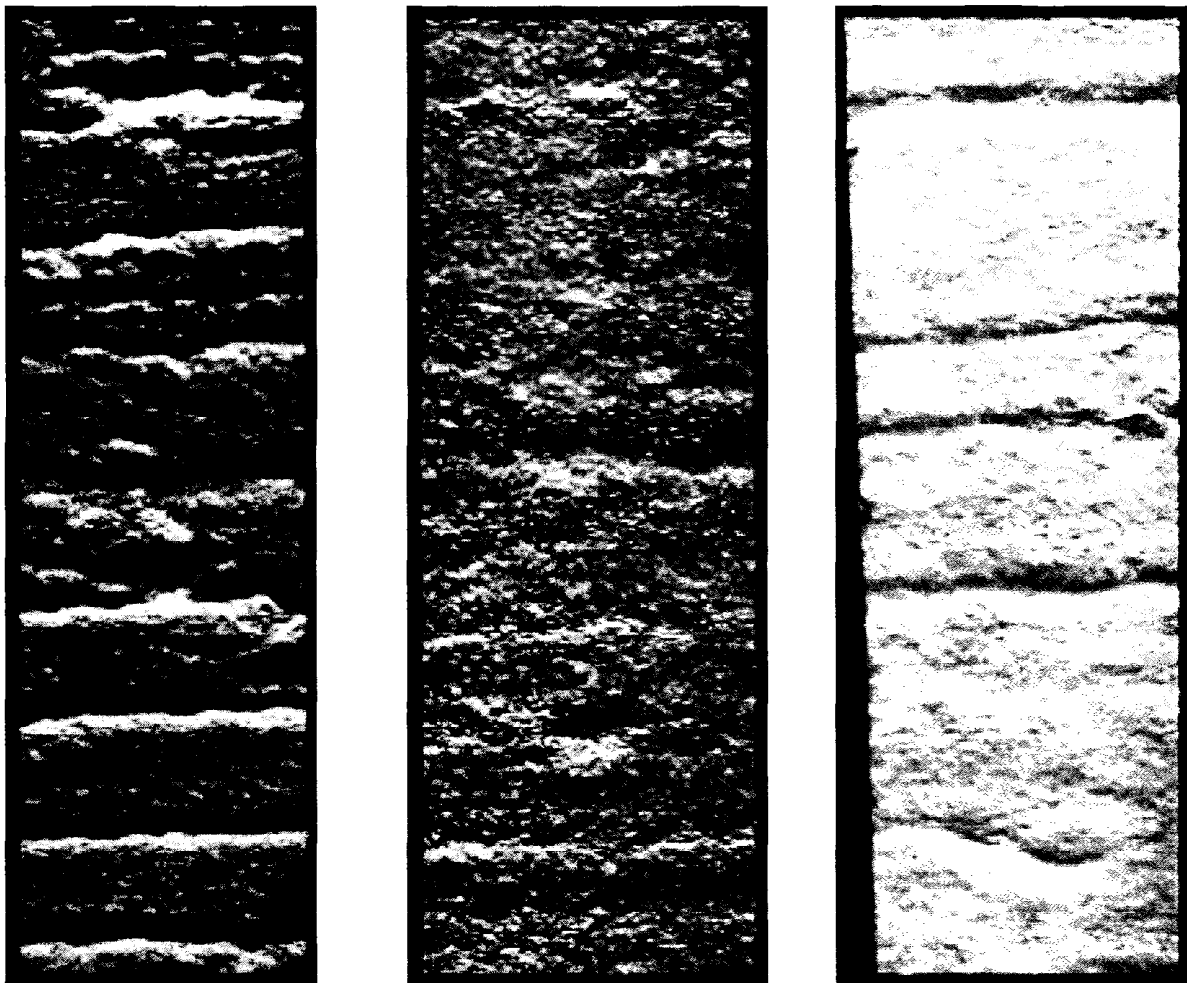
Внешний вид "следов качания" на поверхности непрерывнолитого слитка
